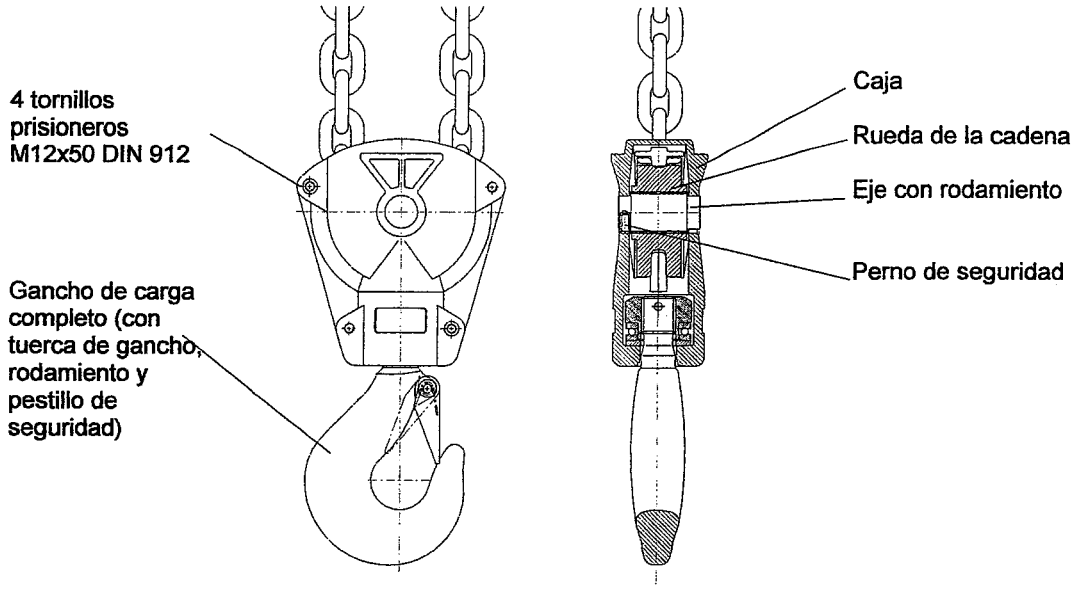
Estructura de la caja del gancho de cadena 16x45 mm
